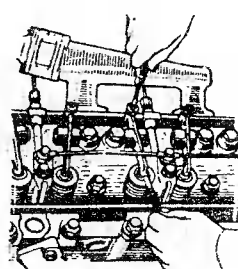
Регулировка зазора клапанного механизма
